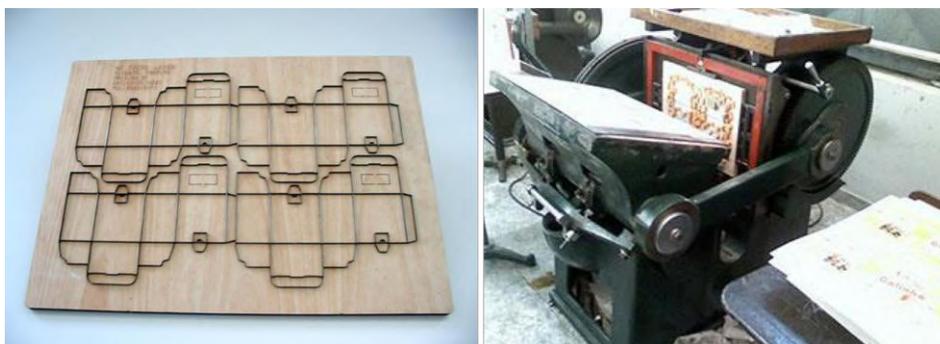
Faca e máquina para corte e vinco (Fontes: www.chocoladesign.com e www.neimaq.com.br)
